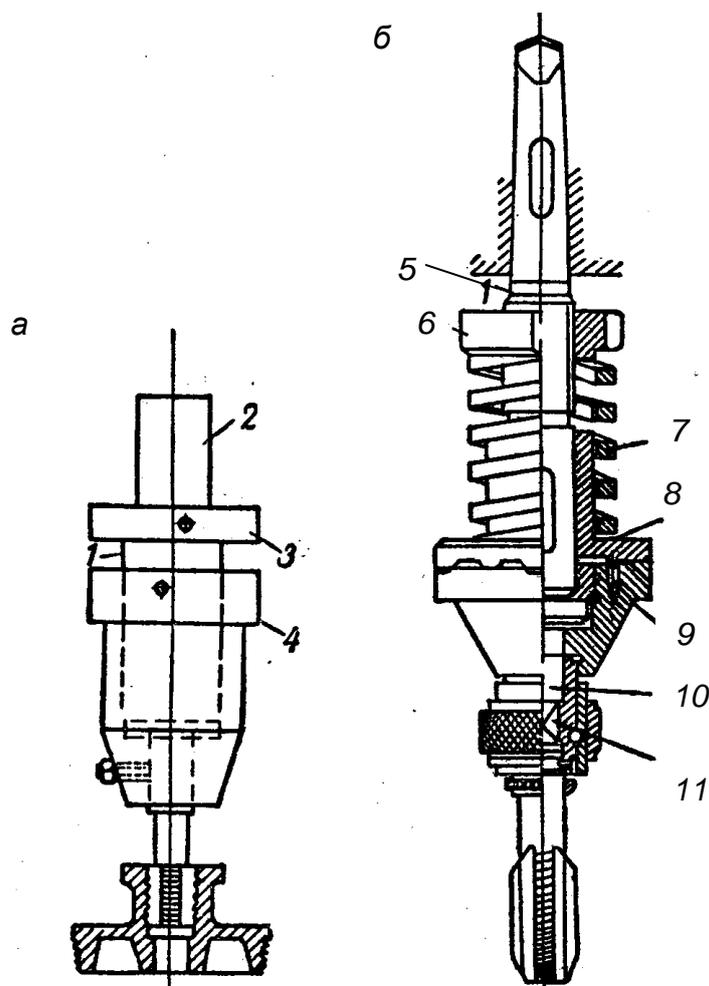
Виды самовыключающихся патронов: а – с выключением от упора; б – с выключением при перегрузке; 1, 3 – шпилька; 2 – оправка; 4 – выдвигаемая часть патрона; 5 – валик; 6 – гайка; 7 – пружина; 8, 9 – полумуфта; 10, 11 – втулка
